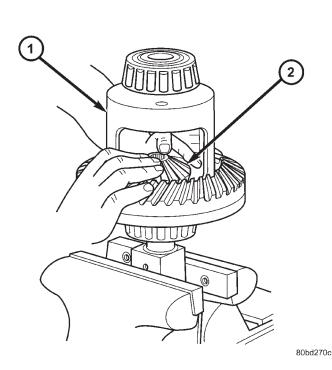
CONJUNTO DE EMBRAGUES Y ENGRANAJE LATERAL INFERIOR
